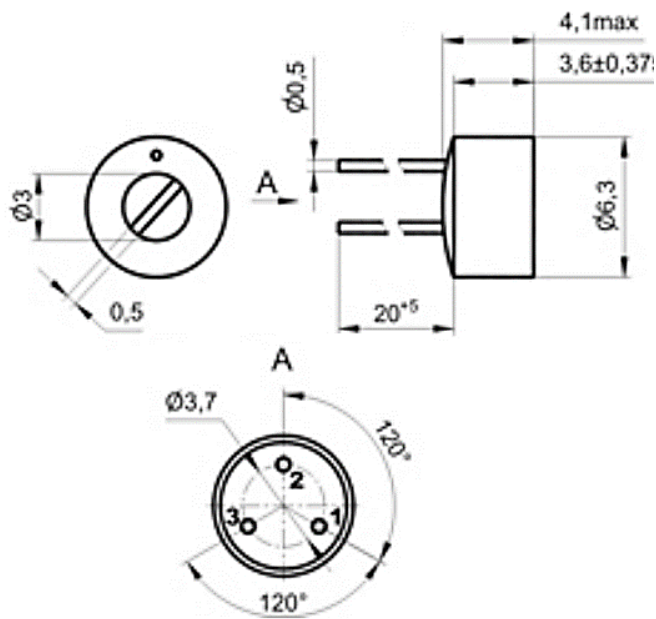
Габаритні розміри підстроювального резистора СПЗ-19А
